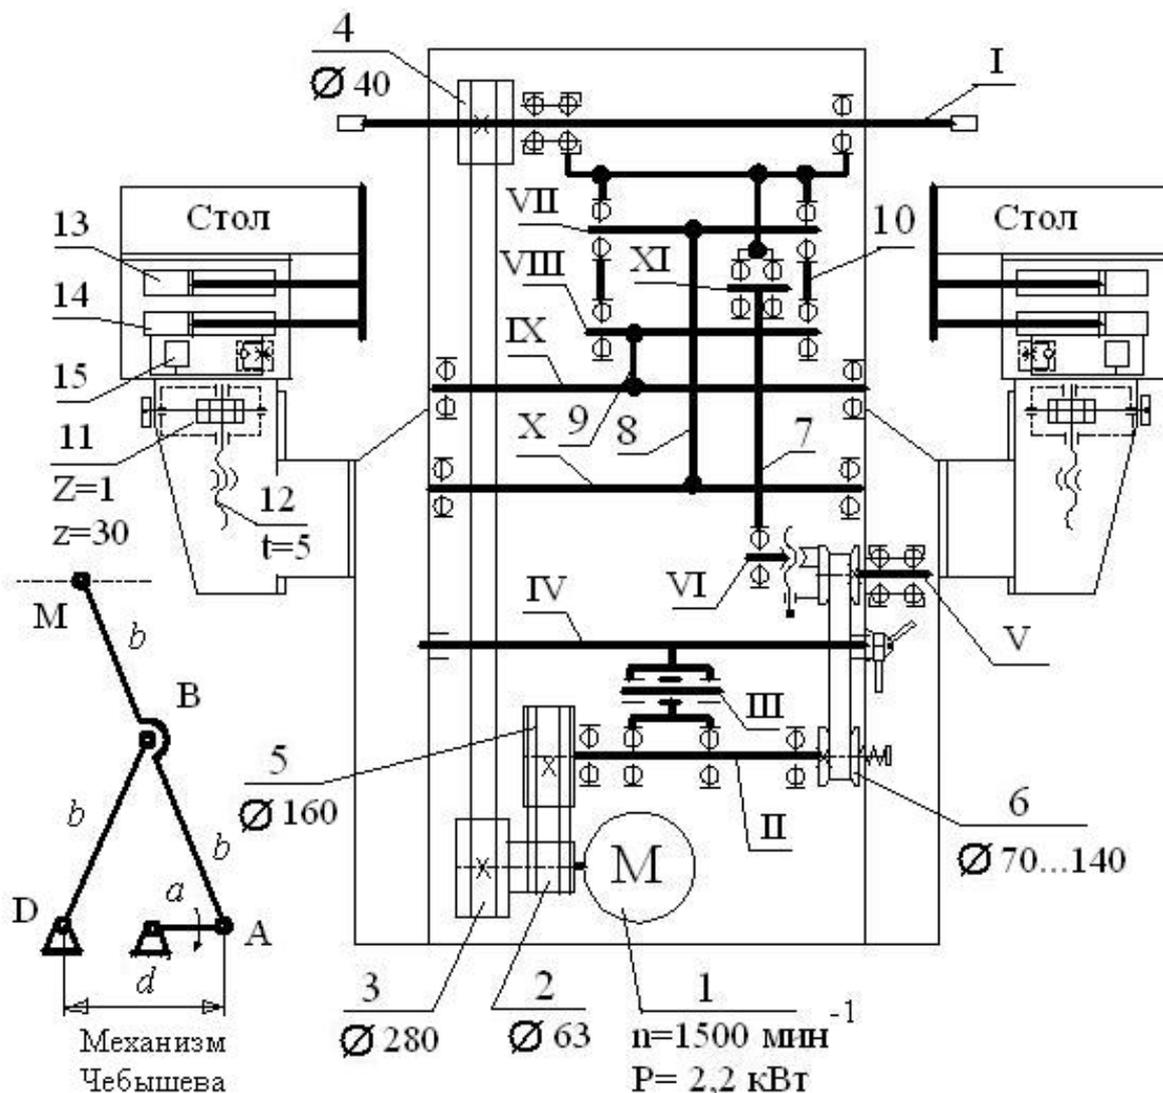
Кинематическая схема горизонтального сверлильно-фрезерного пазовального станка СвПГ-2
